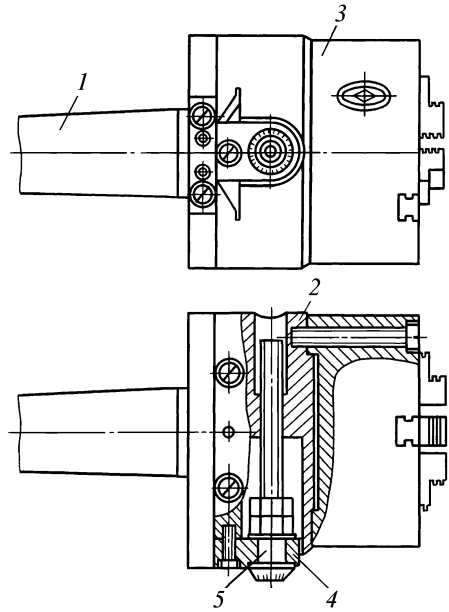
Патрон для обточки и расточки эксцентриков
